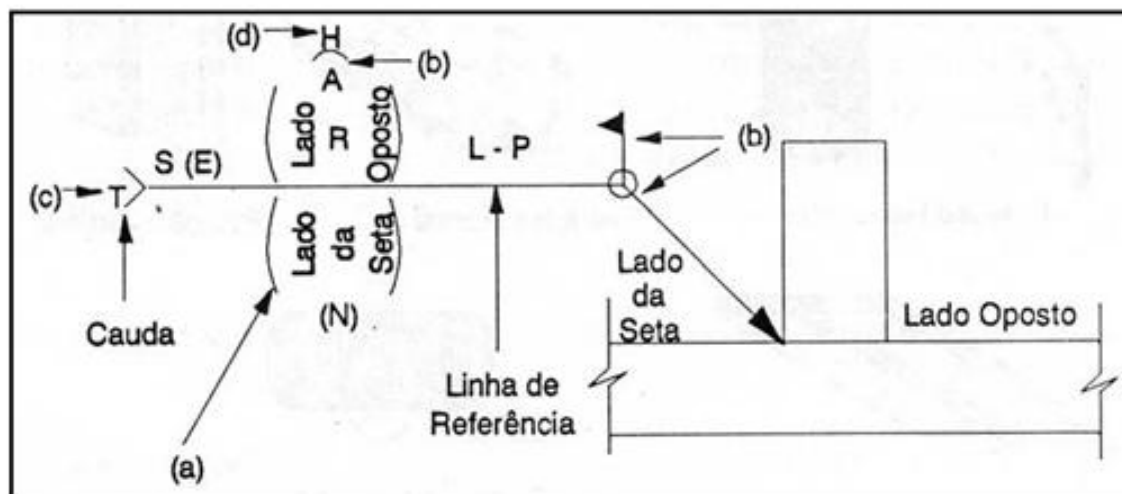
Localização dos elementos de um símbolo de soldagem.
